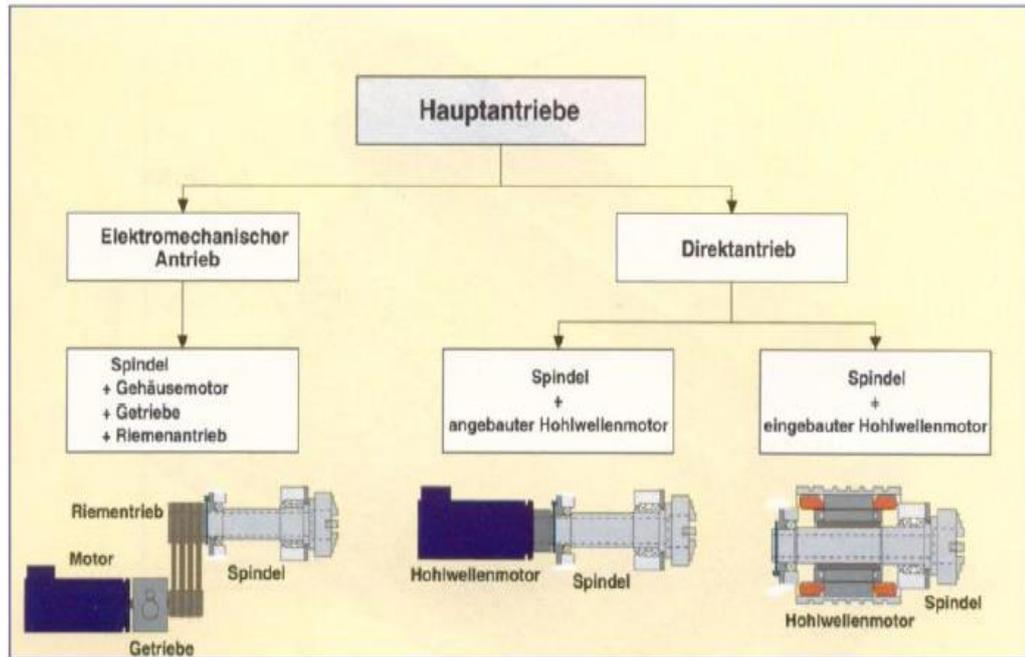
Hauptantriebe einer Werkzeugmaschine [Wißuwa2006, S.3]
